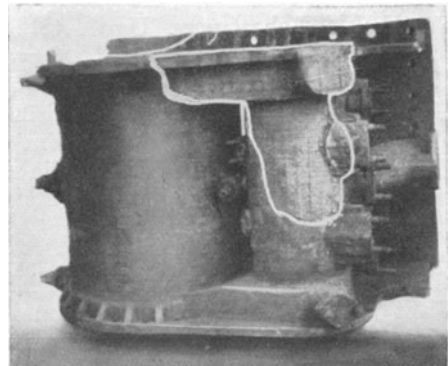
Lokomotivzylinder (Abb. 321) nach der Schweißung.
